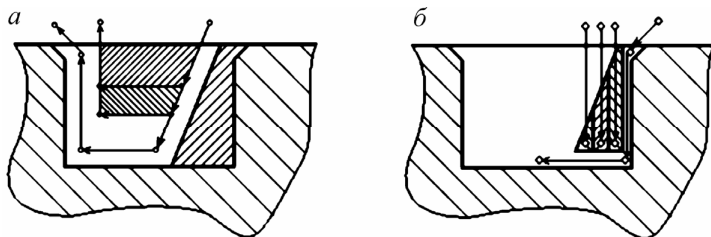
Схема перемещения инструмента при обработке наружных прямоугольных канавок ($b > 9B$):
